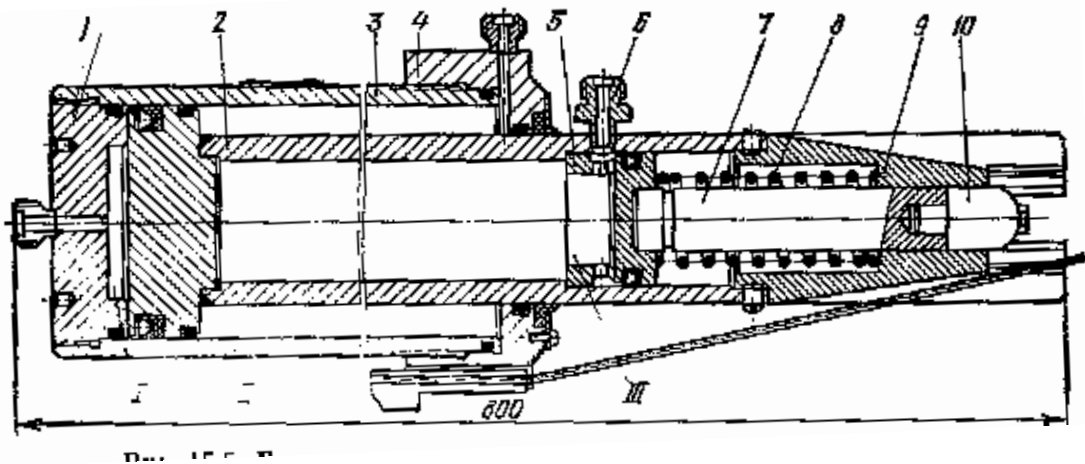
Гидродомкрат СМЖ-81 для натяжения пучков арматуры:
